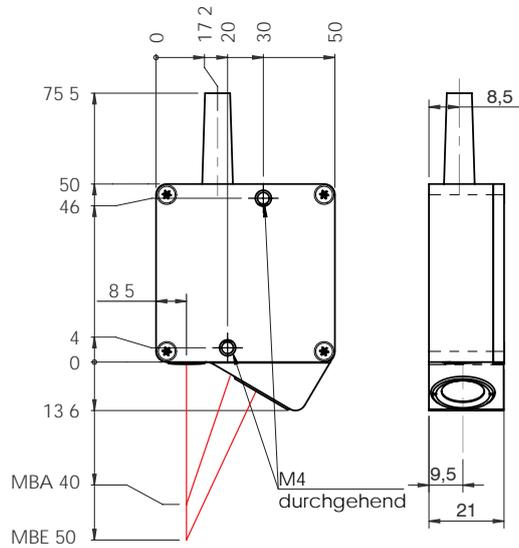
Maßzeichnung LD1610-10 / LD1630-10
